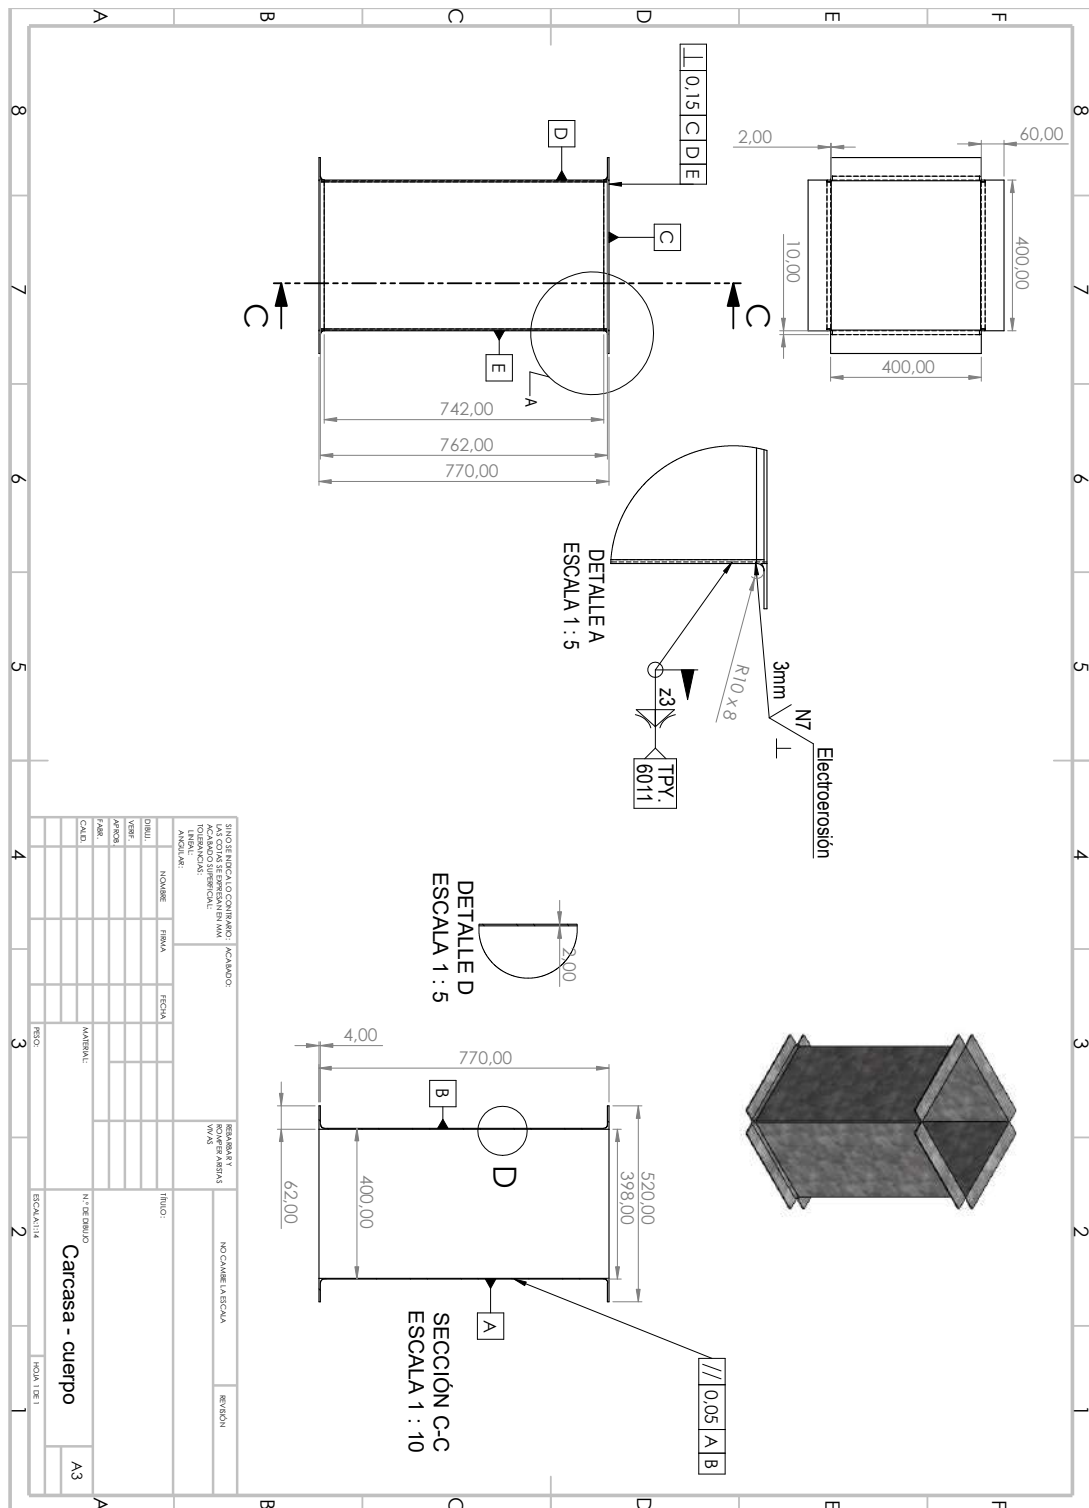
Plano de la carcasa - cuerpo. Fuente: Los autores.
